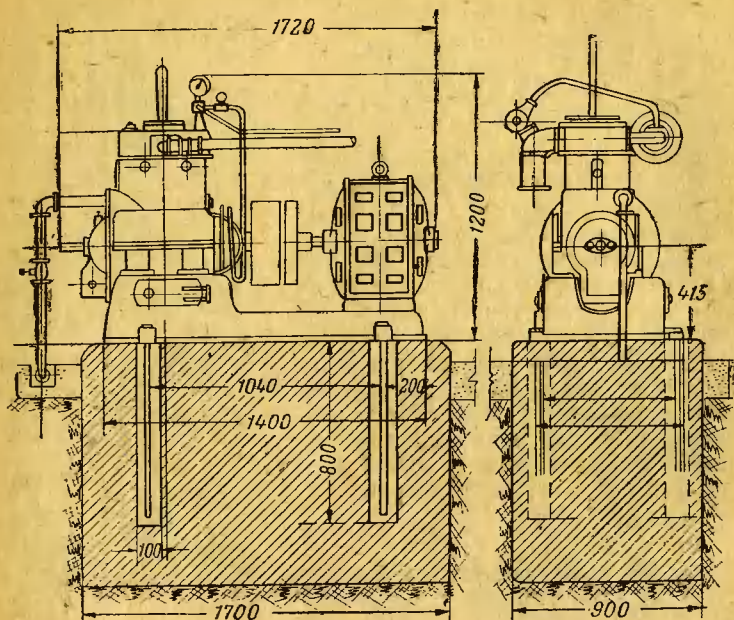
Вертикальный одноцилиндровый воздушный компрессор марки ВВК-155 (Мелитопольского завода)
